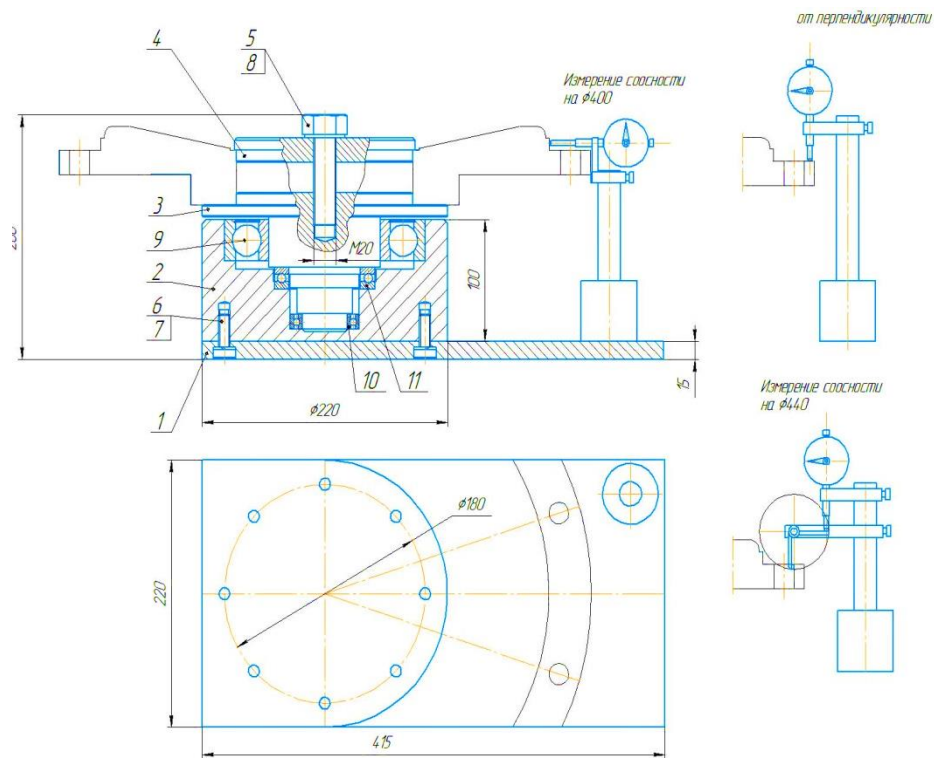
Принципиальная схема контроля детали «Крышка насоса» в приспособлении
